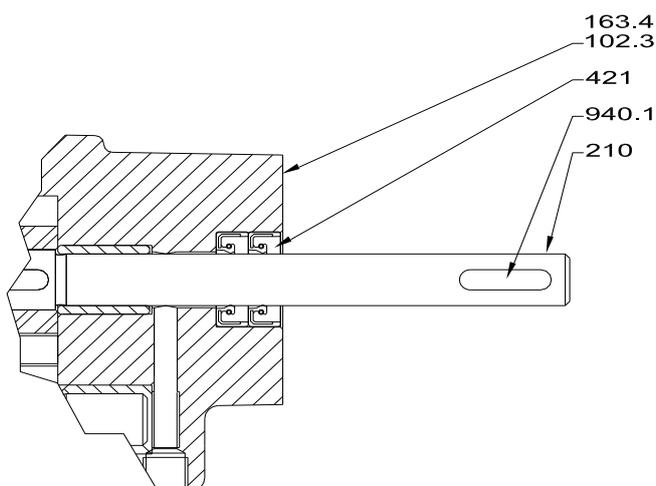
Desenho em Corte bomba FBE c/ retentor
